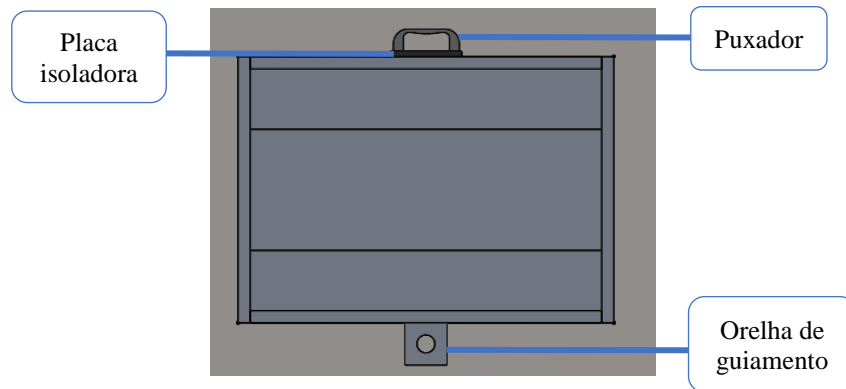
"Vista de topo do conjunto prato e molde inferior"
